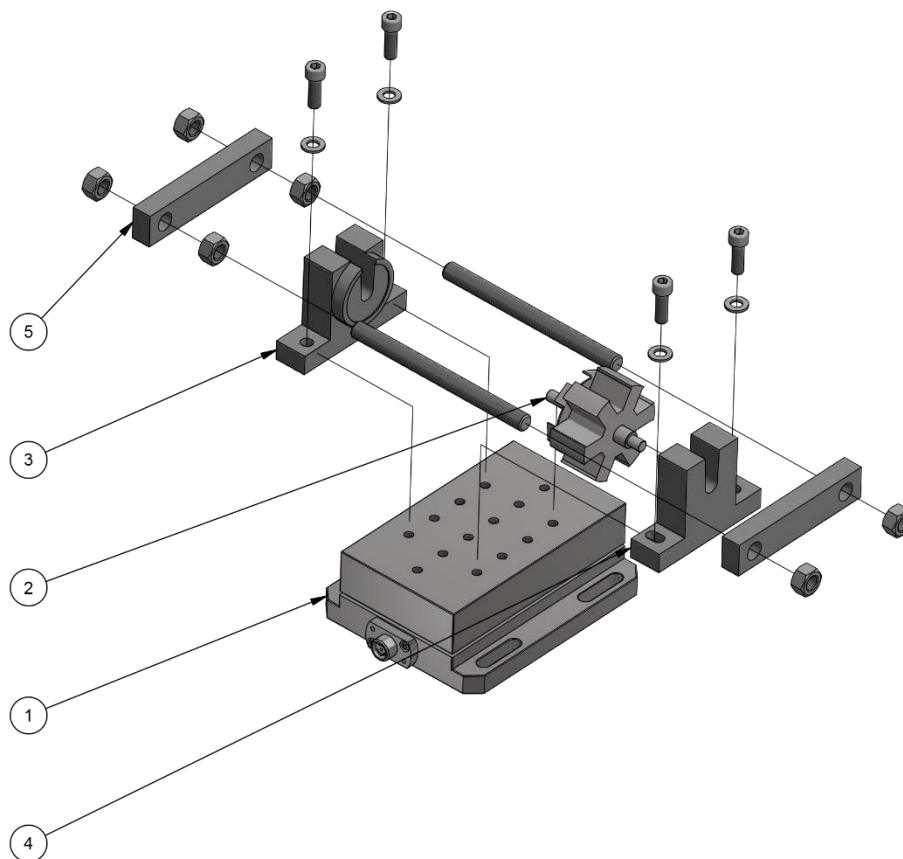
Vista explodida do dispositivo concebido para a fixação do rotor à plataforma dinamométrica durante o ensaio de maquinação.
